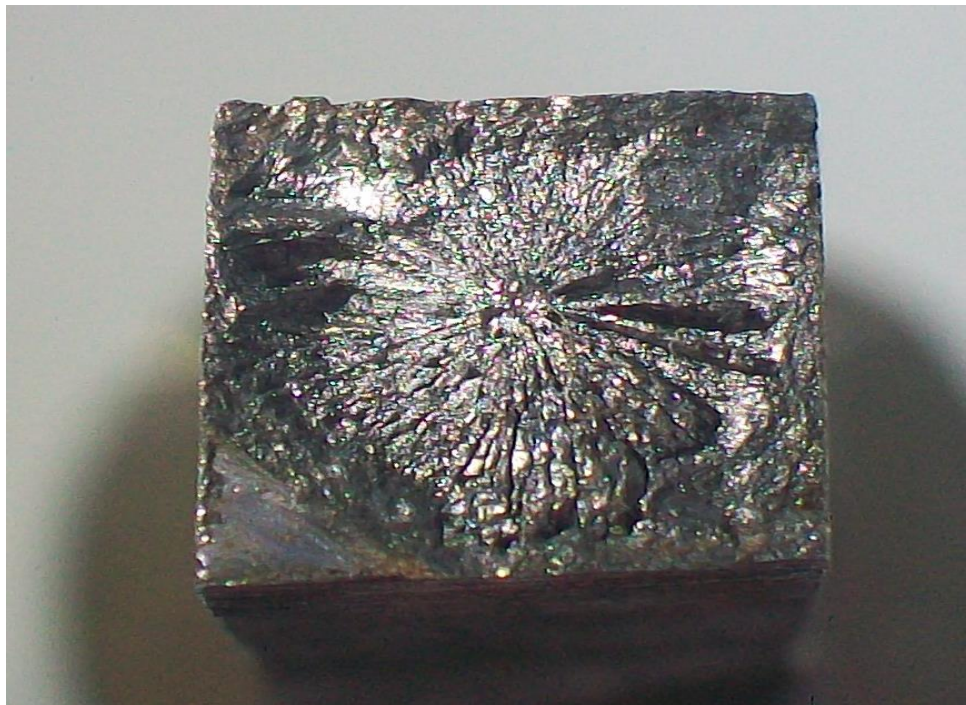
Sección transversal de la rotura de la probeta 5.
